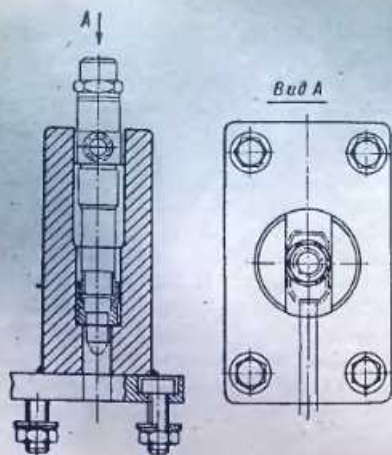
Приспособление ЛМ9690-170 для сборки и разборки форсунки
